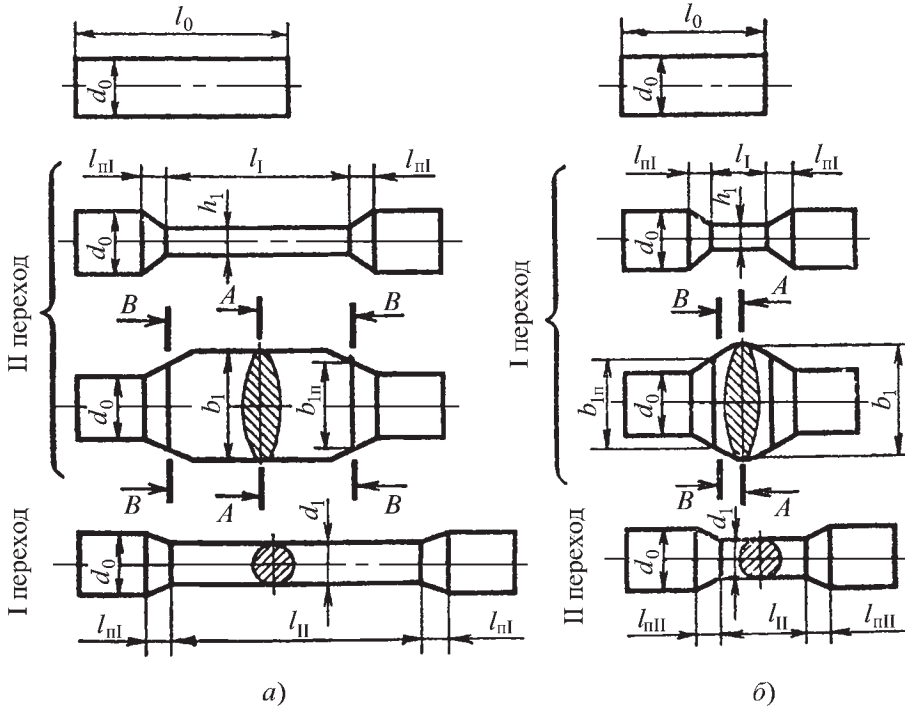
Переходы при вальцовке за два прохода заготовок с двумя необжимаемыми головками: а — длинная заготовка; б — короткая заготовка
